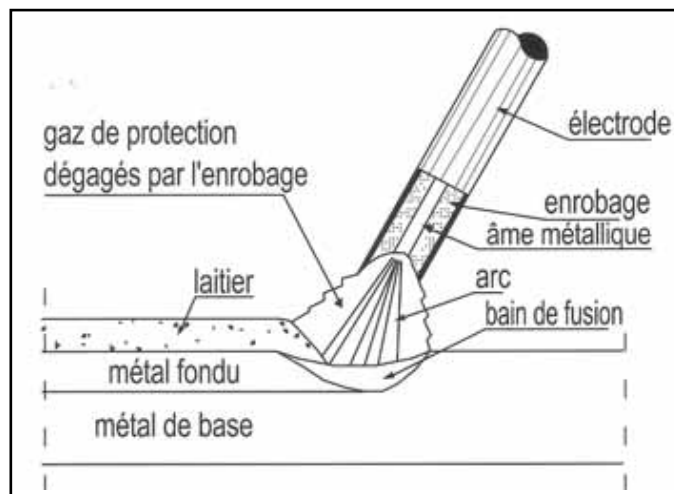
Principe du soudage à l'arc avec électrode enrobée (bibliographie [6]).
